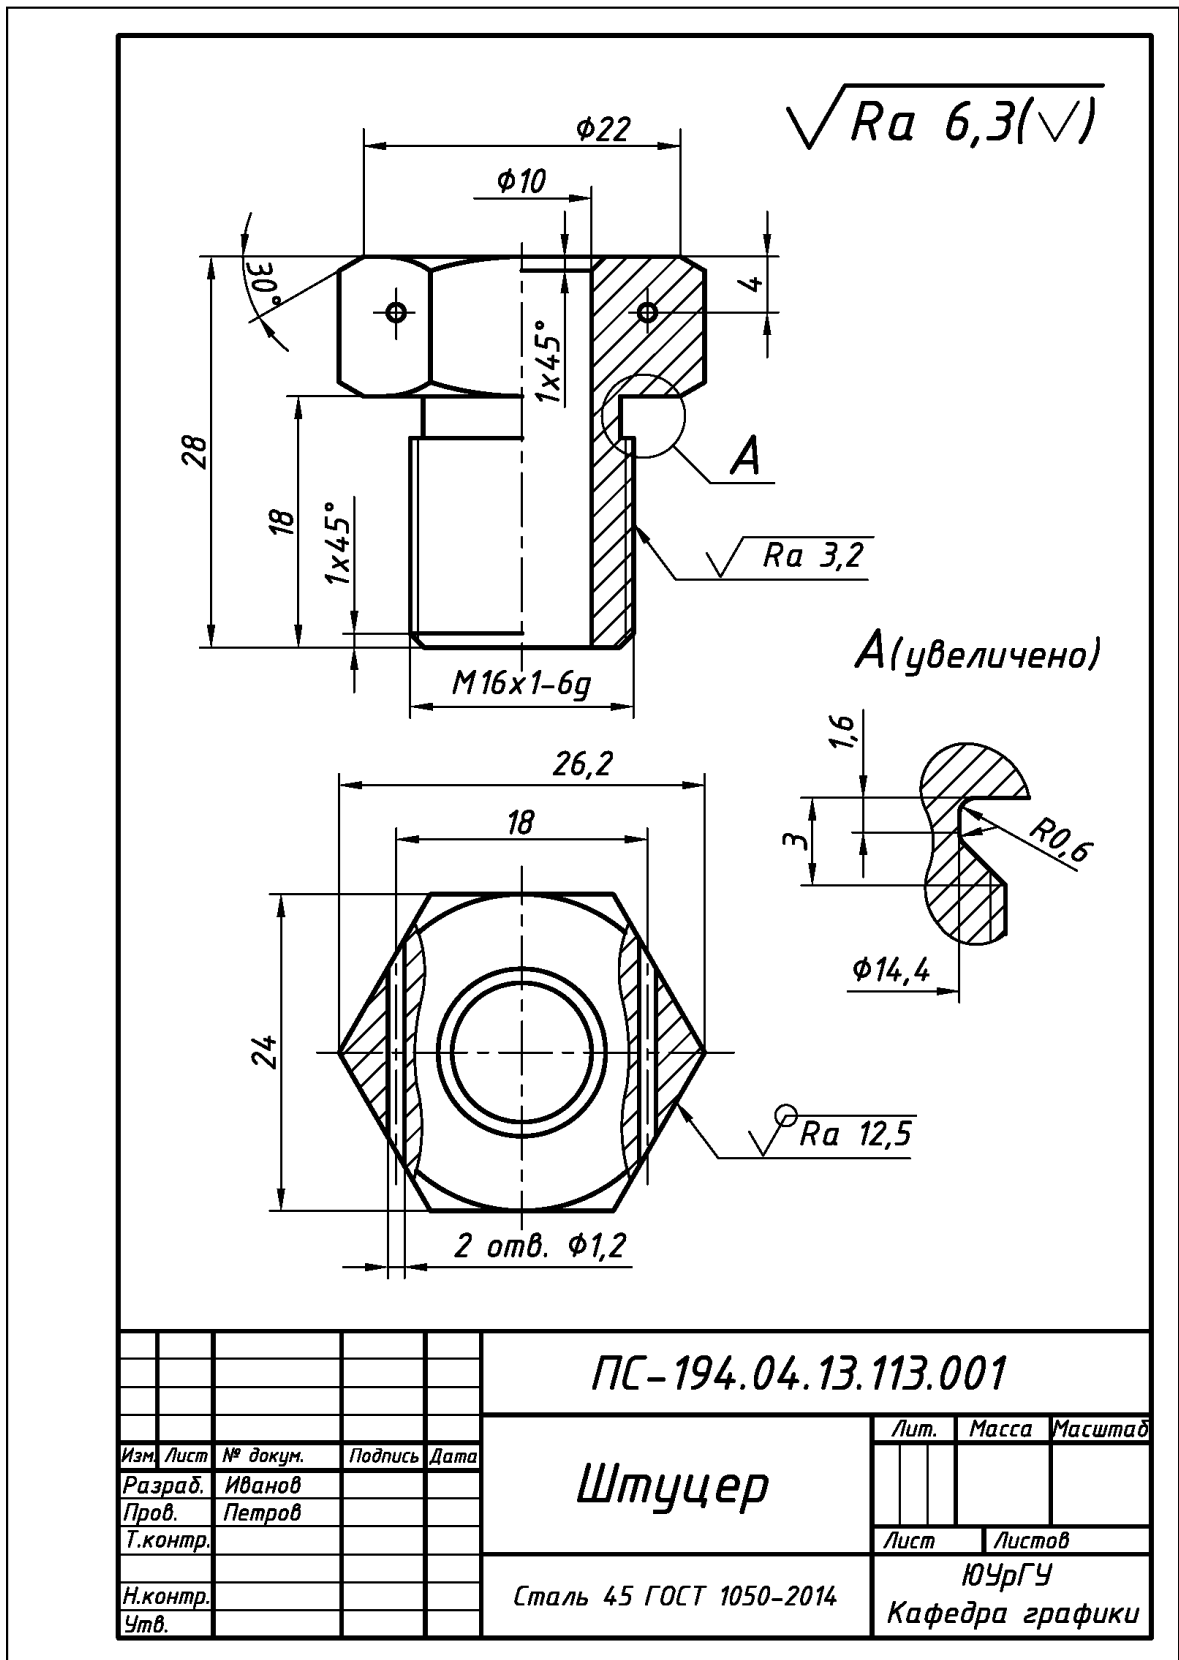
Пример выполнения и оформления эскиза детали «Штуцер», изготовленной из металла токарно-фрезерной обработкой
